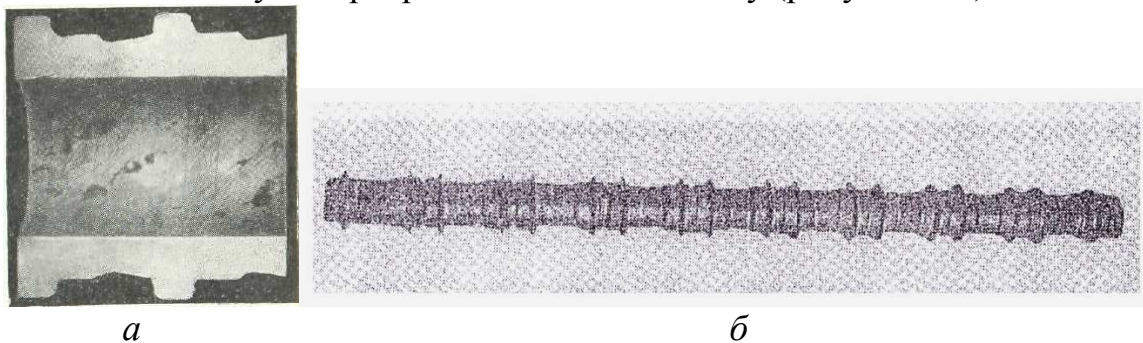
Вид заготовок с РПП: а- микрошлиф ; б- вид заготовки с РПП для велосипедной втулки
